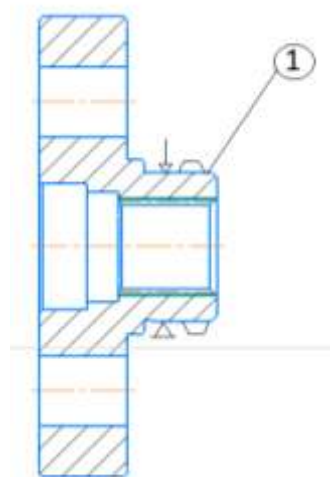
Колесо зубчатое (поверхность для захвата промышленным роботом)
